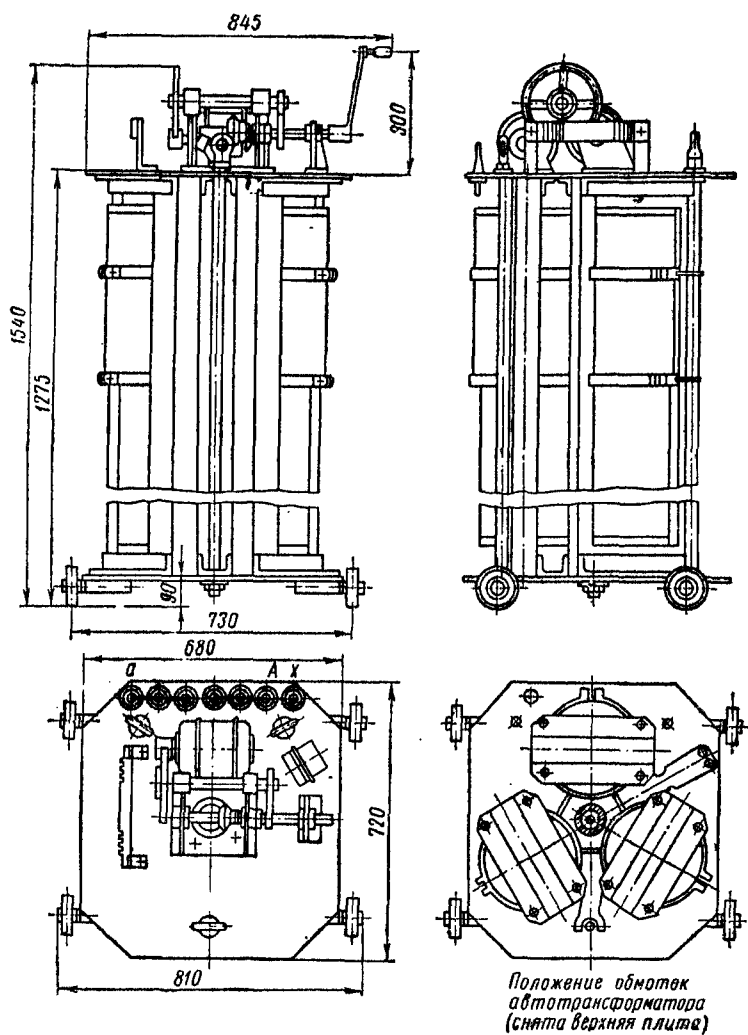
Внешний вид и габаритные размеры регулировочного автотрансформатора АОСК-25/0,5
